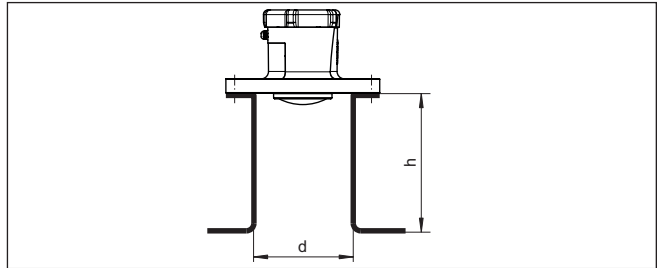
Montage de la rehausse en cas de dimensions de rehausse différente
